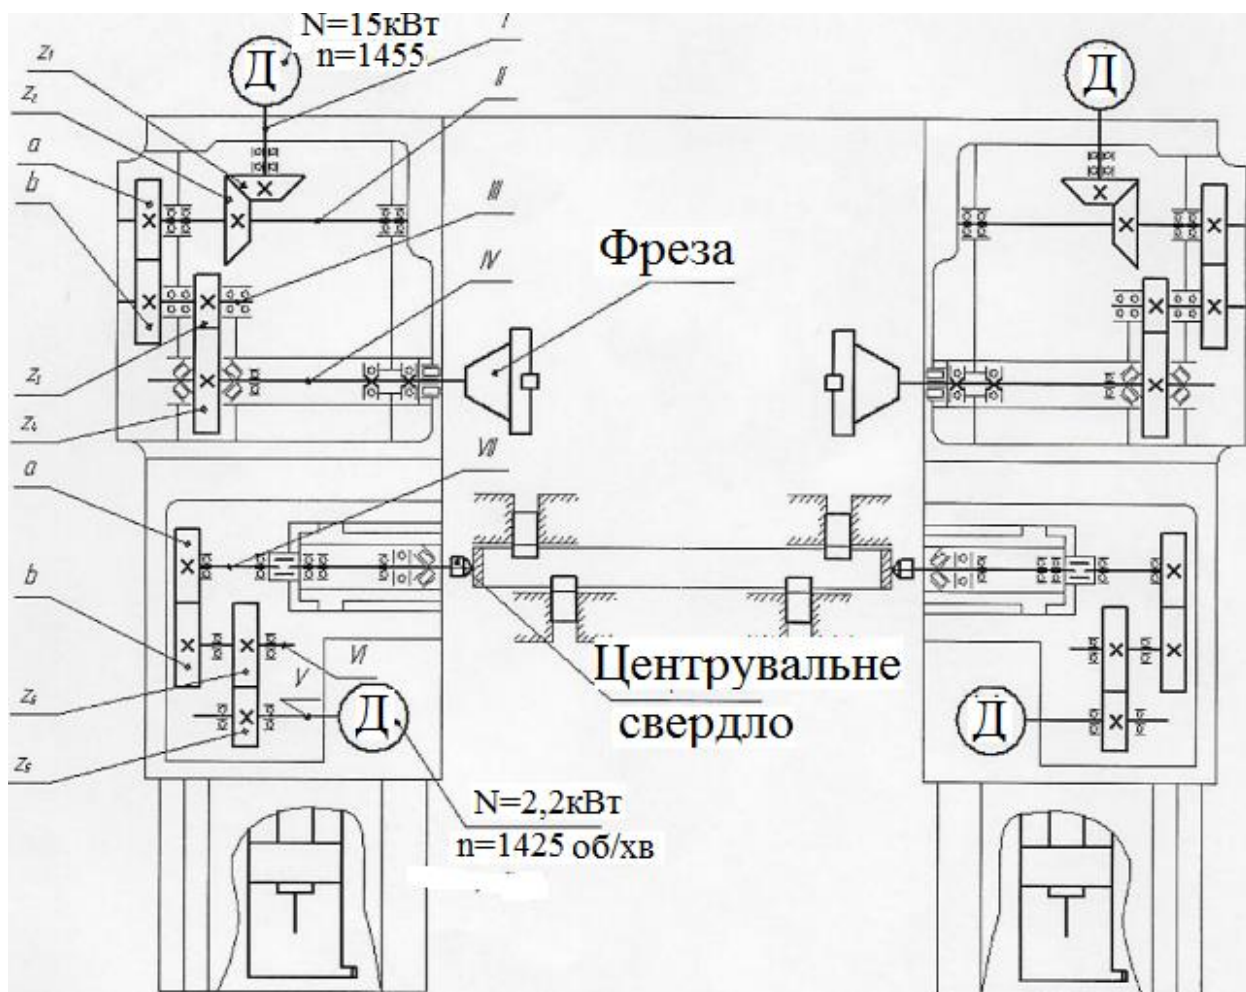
Кінематична схема фрезерно-центрувального верстата-напівавтомата
